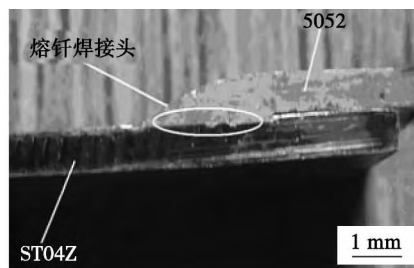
铝钢激光熔钎焊接头截面形貌
